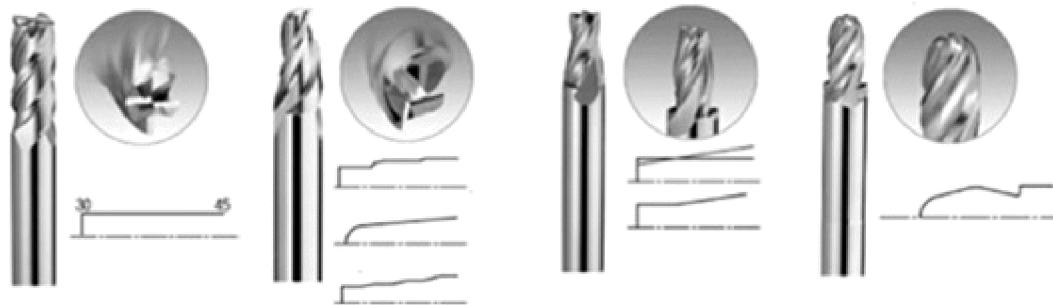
Фрезы, получаемые на шлифовальнозаточных центрах с ЧПУ
